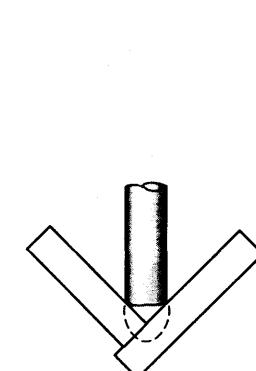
Сварка угловых соединений с опиранием покрытия
